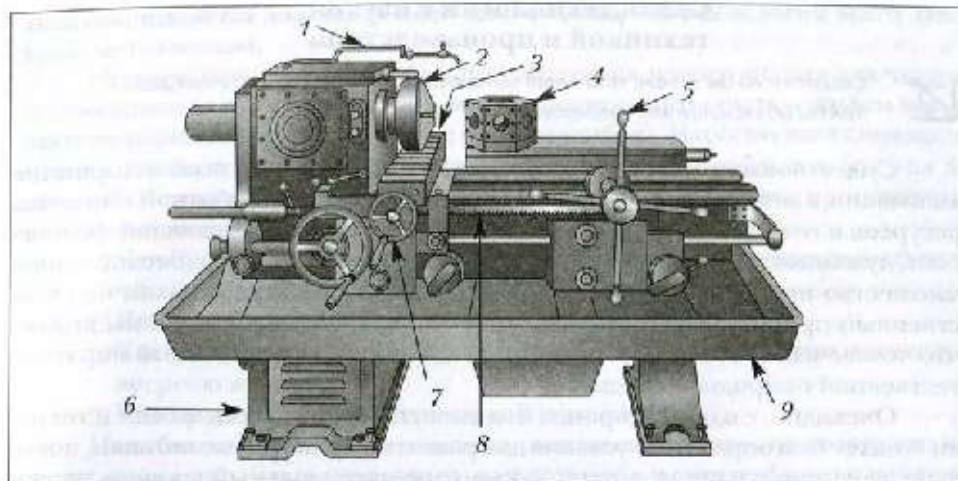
Токарный станок с револьверной головкой первой половины XX века: 1 — подвод смазочно-охлаждающей жидкости; 2 — зажимной патрон; 3 — поперечная каретка; 4 — револьверная головка; 5 — ручной привод перемещения головки; 6 — станина; 7 — суппорт; 8 — зубчатая рейка механизма продольной подачи; 9 — поддон
